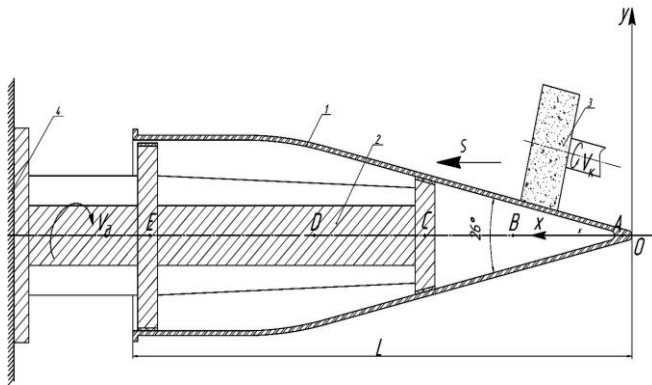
Схема зовнішньої обробки виробу: 1– заготовка; 2–пристрій; 3 – шліфувальний круг; 4 – шпиндельний вузол верстата
